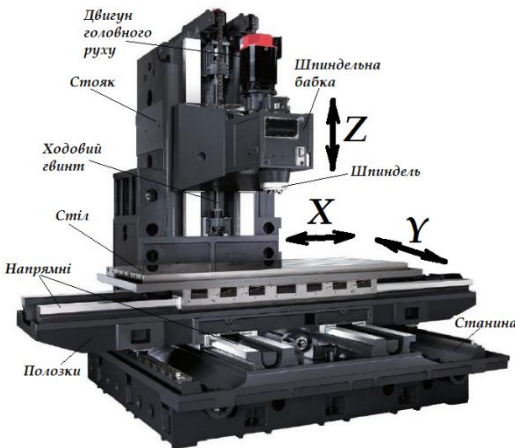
Будова фрезерного верстата з ЧПК
